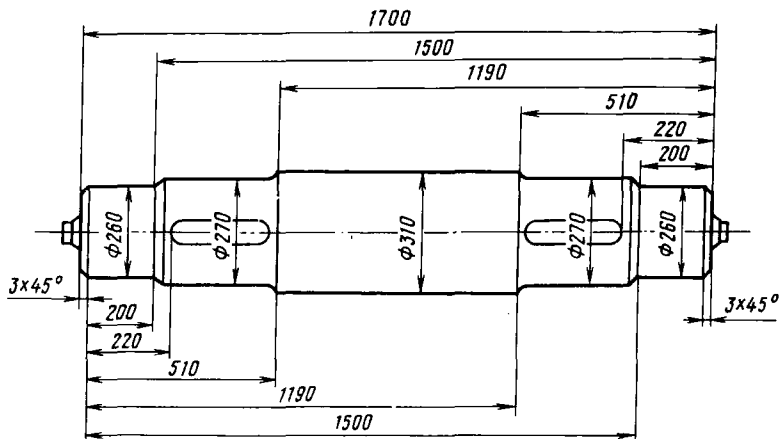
Главный вал главного редуктора эскалаторов ЛТ-2 и ЛТ-3
